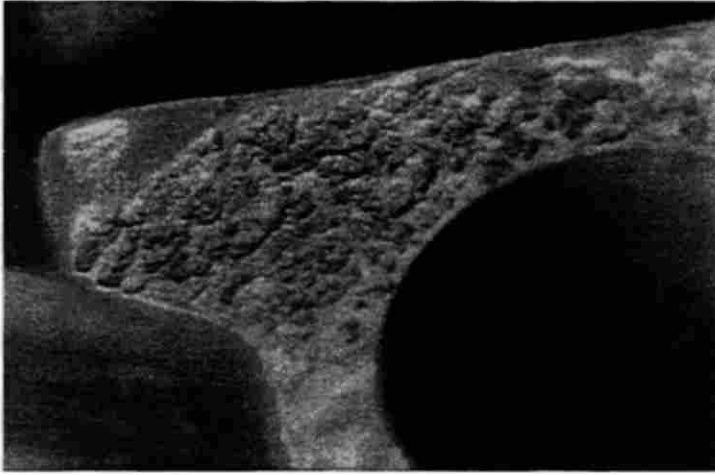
Corrosión por rozamiento en la parte de la raíz del álabe.
